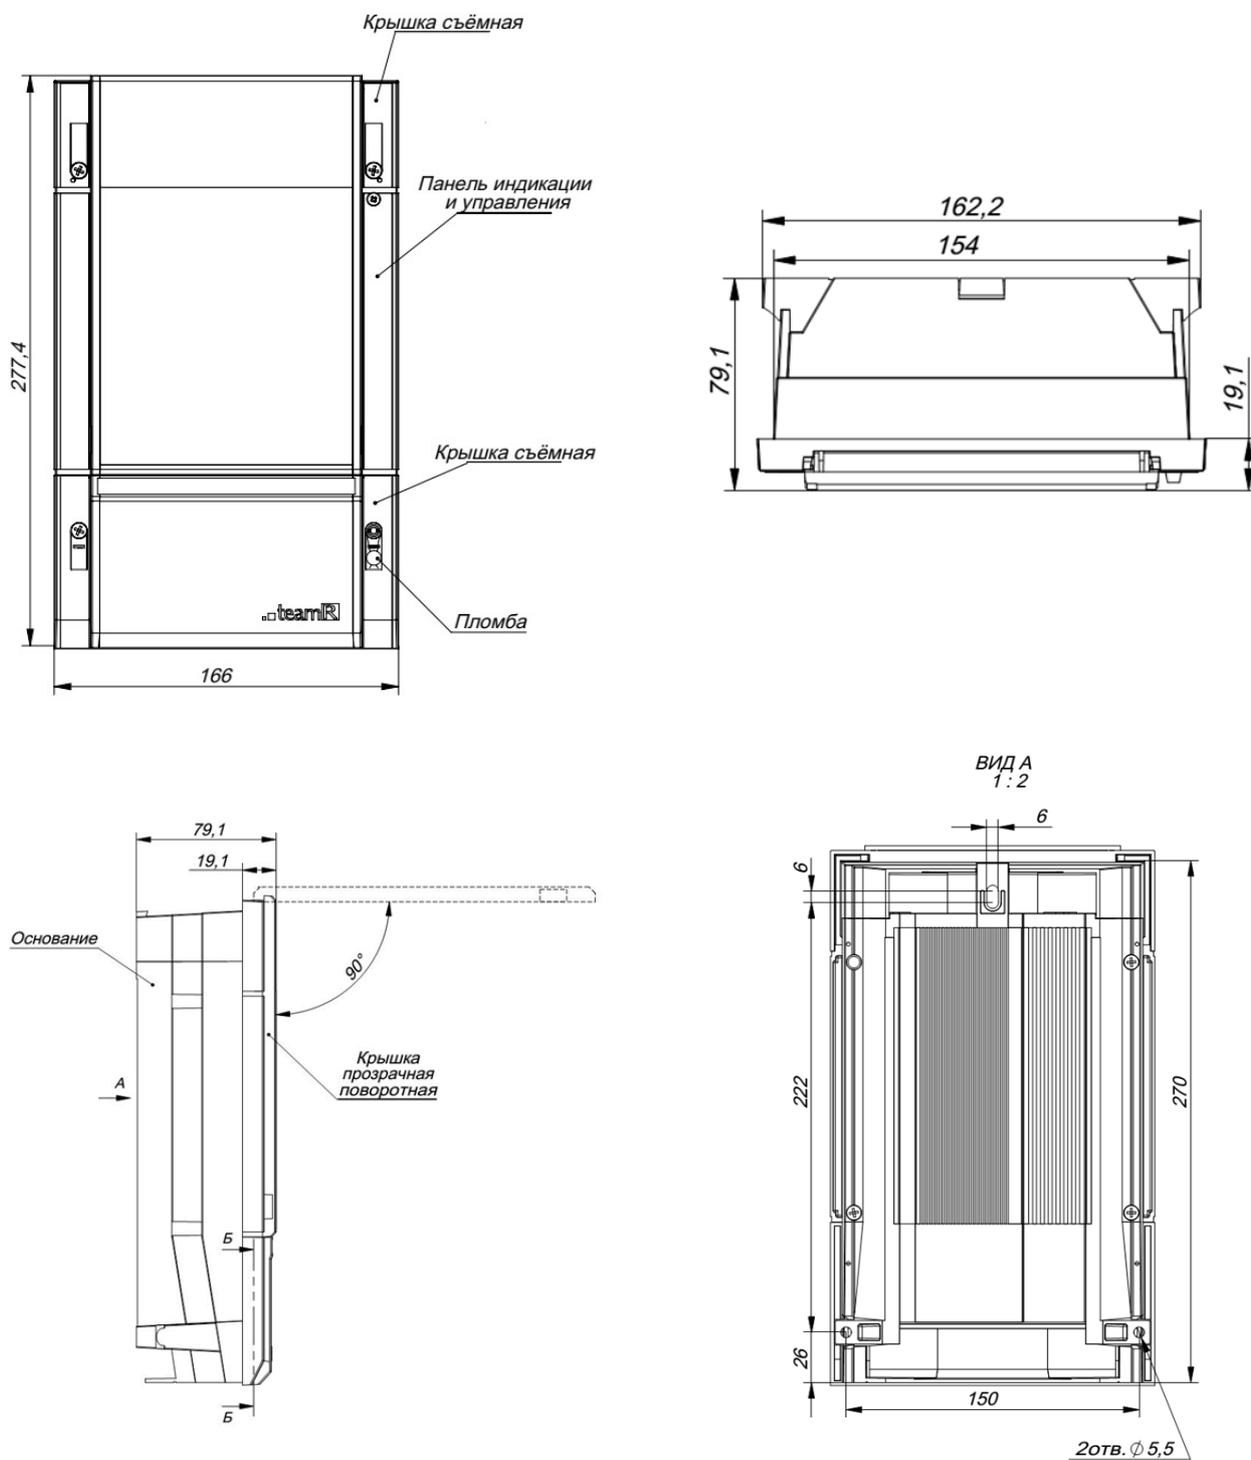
Габаритные размеры и вид счетчика со стороны крепления
